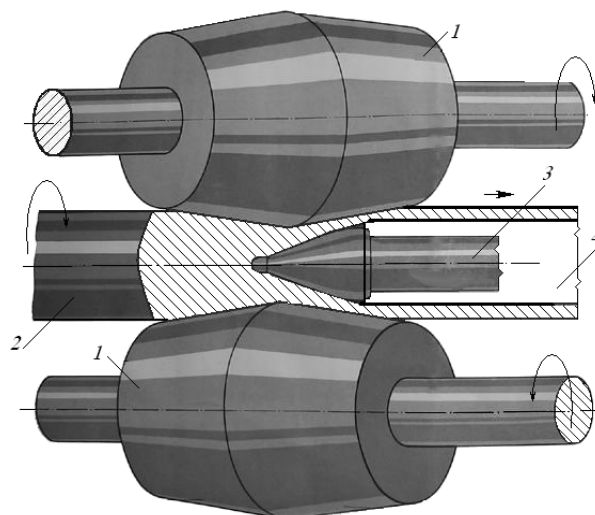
Поперечно-винтовая прокатка заготовки трубы (гильзы):
